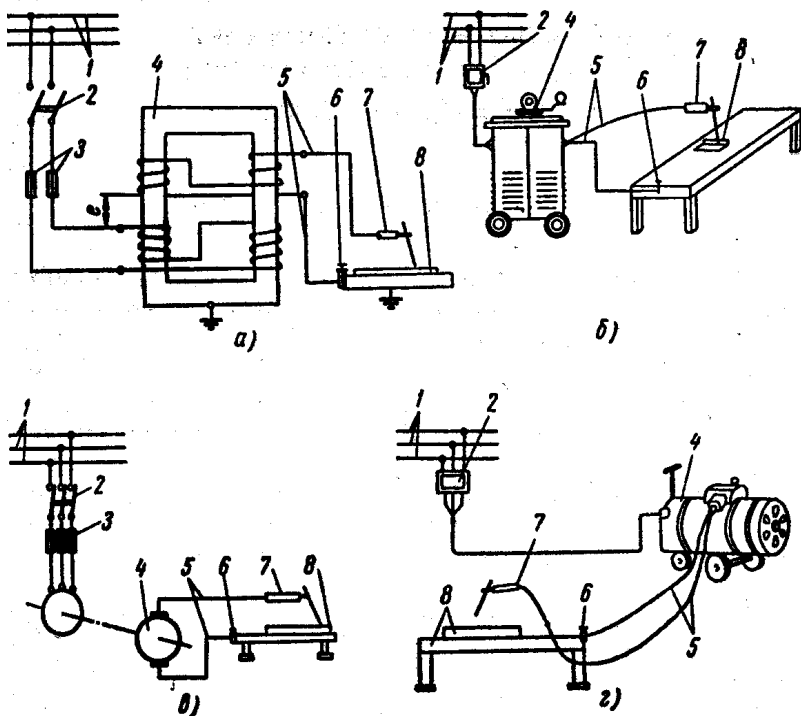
Схемы поста для ручной дуговой сварки:
